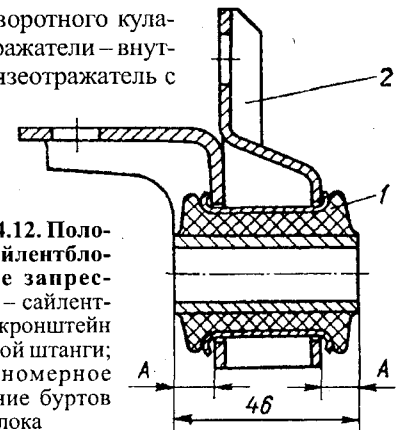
Положение сайлентблока после запрессовки: 1 – сайлентблок; 2 – кронштейн реактивной штанги; А – равномерное выступание буртов сайлентблока
